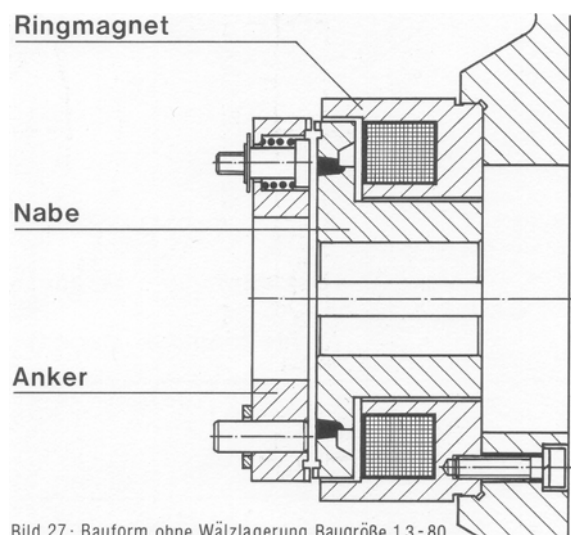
Bauform ohne Wälzlagerung, Baugröße 1,3-80
